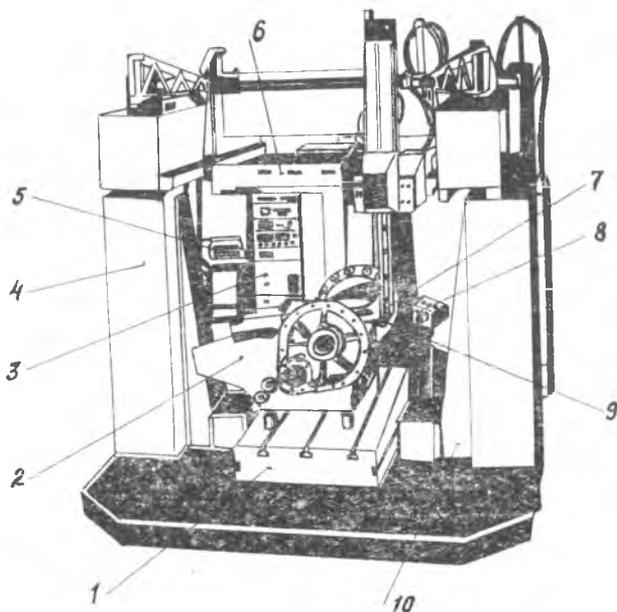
Машина для прецизионного измерения крупногабаритных деталей: 1 — стол; 2 — измеряемая деталь; 3 — устройство для считывания с ленты; 4 — колонна; 5 — устройство для печатания данных; 6 — визуализаторы отметок; 7 — головка-держатель щупа; 8 — пульт и кнопки приведения к нулю; 9 — измерительные датчики
